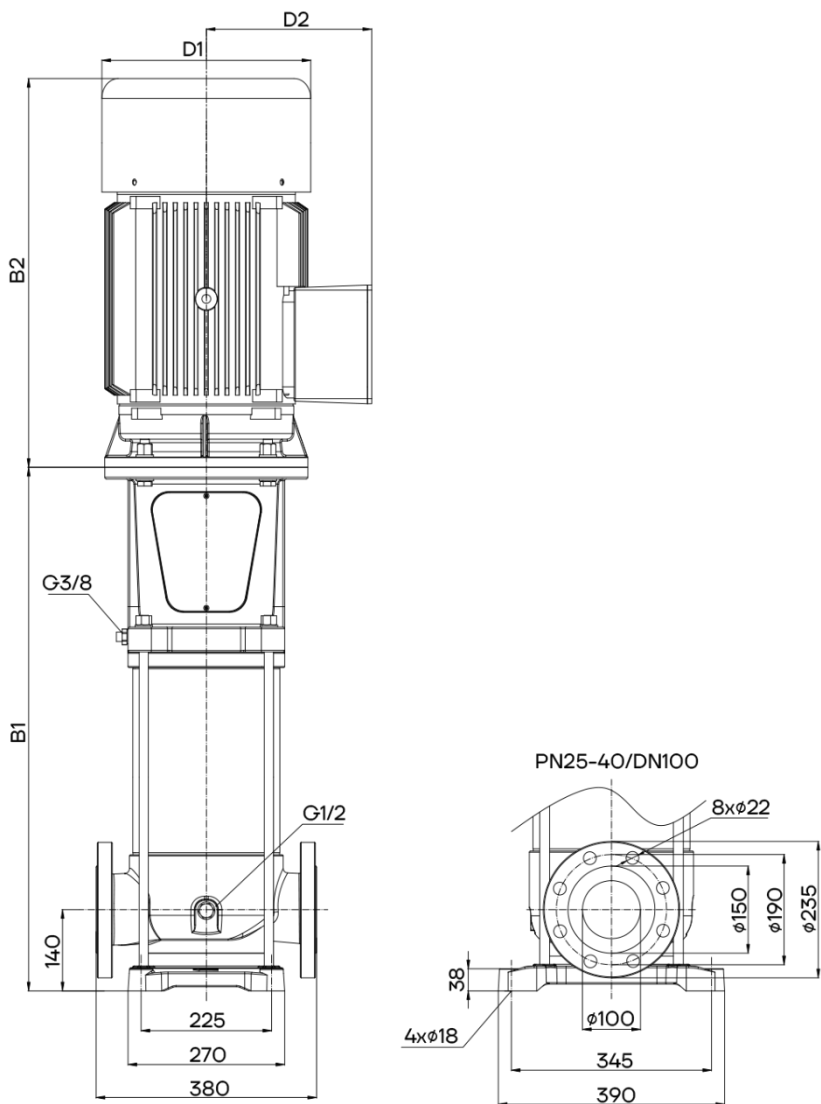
К Габаритно-присоединительные размеры VMB(F)-H 100
